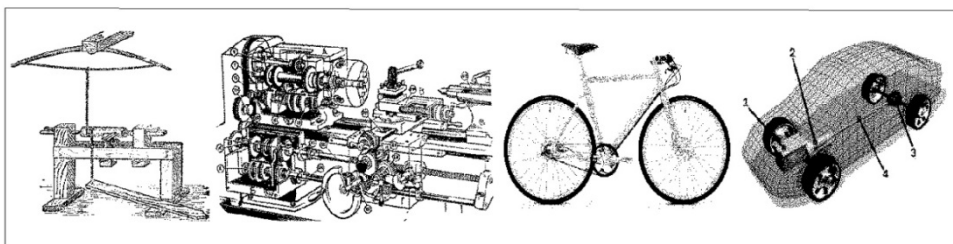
Логічний ряд зображень для сприйняття поняття «привод машин» (зліва направо): давній токарний верстат з лучковим приводом; токарно-гвинторізний верстат ТВ-6; велосипед; трансмісія легкового автомобіля: 1 – двигун; 2- коробка передач; 3 - головна передача; 4 – карданна передача
